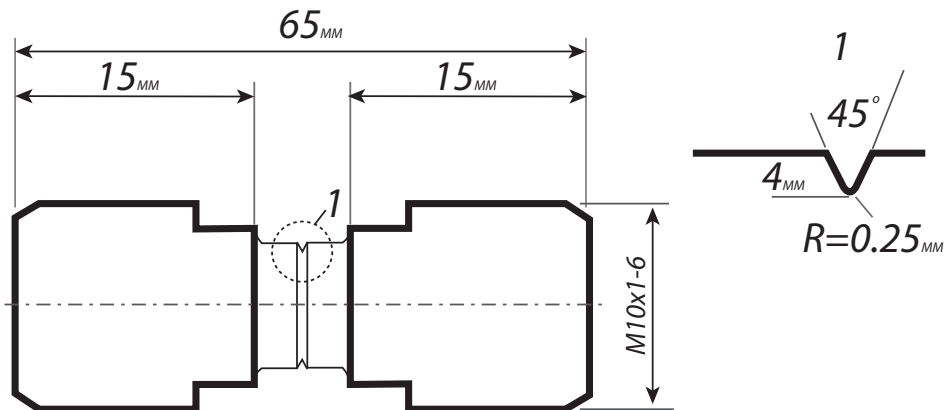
Цилиндрический образец с V-образным вырезом.
